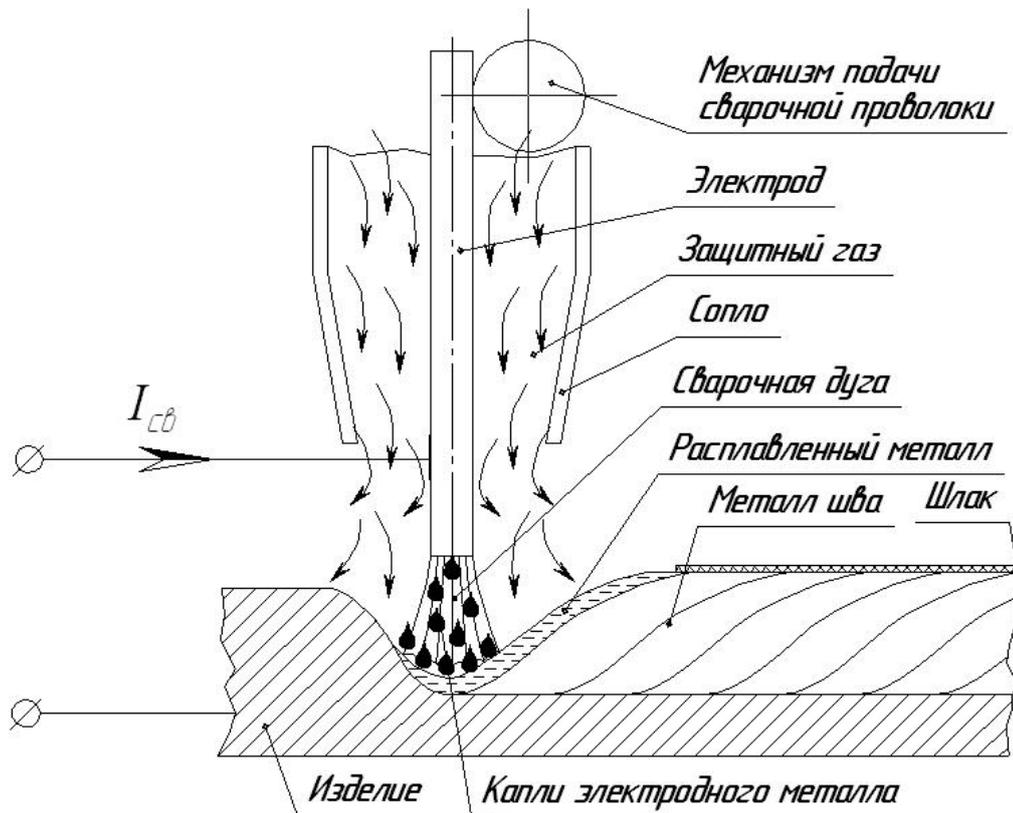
Схема сварки в защитном газе плавящимся электродом
